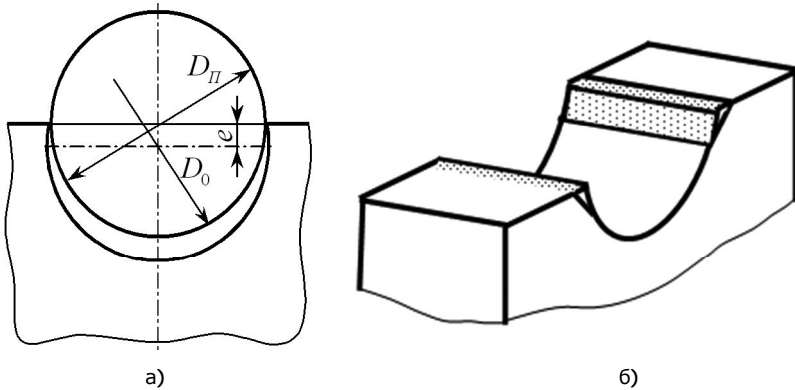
Схема установки зовнішнього кільця вальниці в напівотвір корпусу (а) та припасування поверхонь (б)
